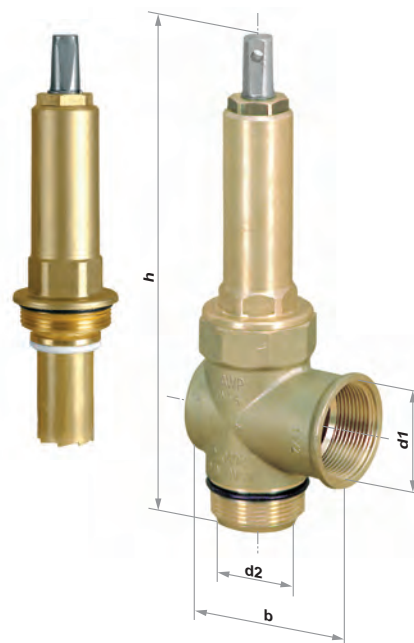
, PN 16 ohne Stanzfräser 1½", 2"
